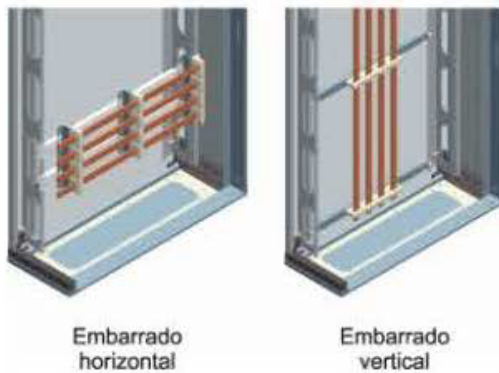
Armario eléctrico con embarrado (horizontal y vertical).
